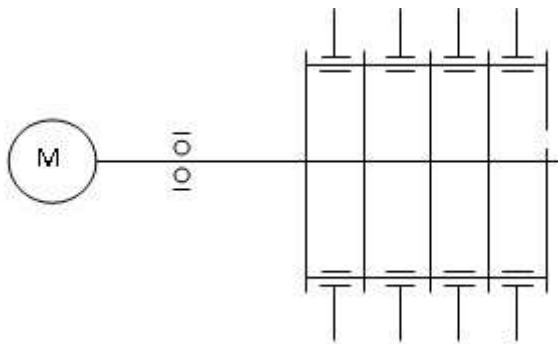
Кінематична схема механізму привода ротора дробарки.
